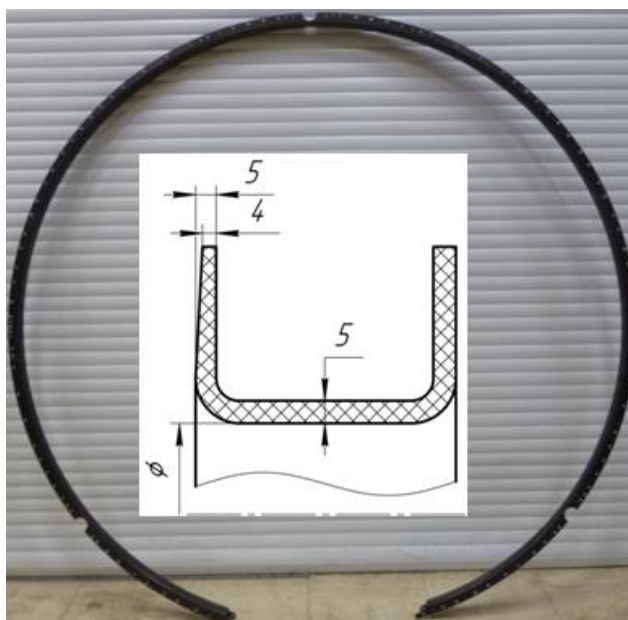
Задний шпангоут реверсивного устройства П-образного профиля
